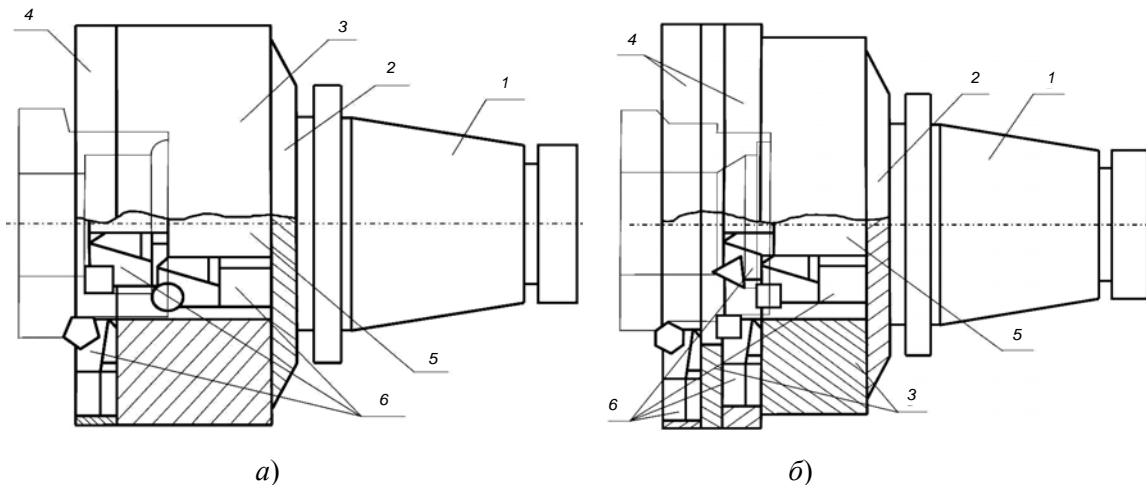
Примеры конструкций универсально-сборного инструмента:
